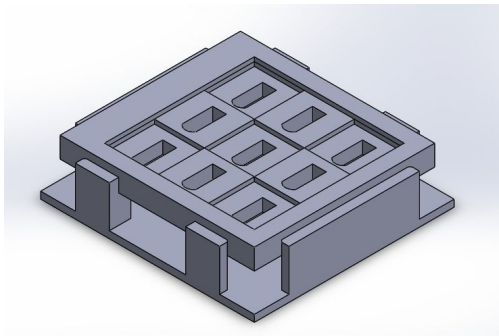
Vista Isométrica Modelagem CAD Tabuleiro 3x3.
